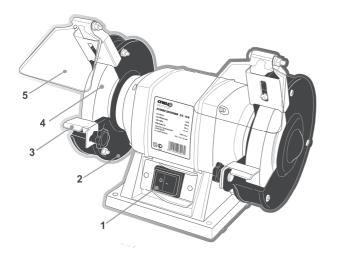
1-выключатель; 2-защитный кожух; 3направляющая подставка; 4 — абразивный круг; 5-защитный экран
